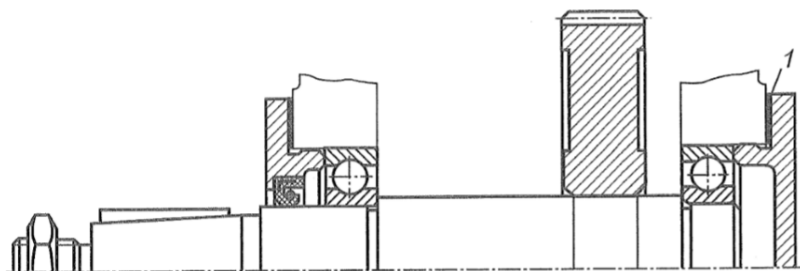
Пример конструкции подшипникового узла с привертными крышками подшипников
